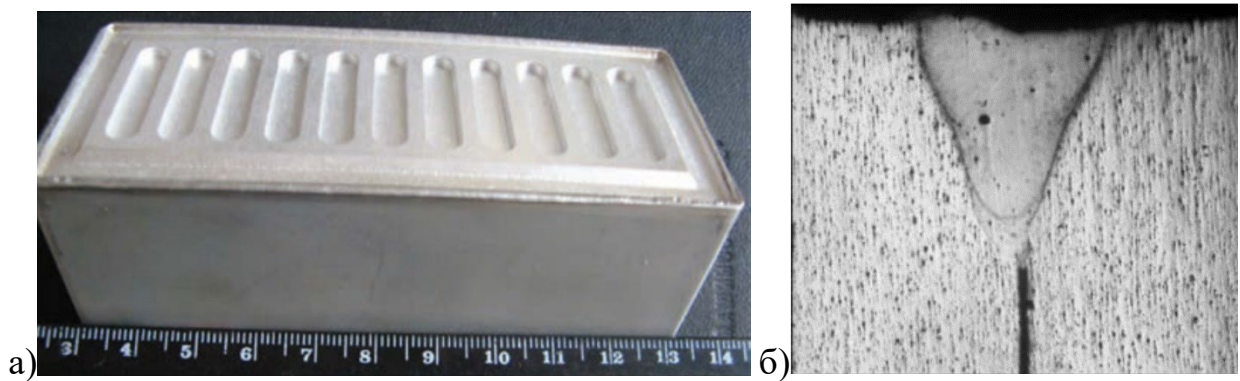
Приклади застосування лазерного та гібридного зварювання з ненаскрізним проплавленням: а) зовнішній вигляд фрагмента корпусу акумулятора з алюмінієвого сплаву АМг6 завтовшки 0,8 мм, з'єданого лазерним зварюванням [89]; б) макроструктура ( $\times 25$ ) перерізу торцевого з'єднання сплаву АМг6 ( $\delta=1,4$  мм), виконаного гібридним лазерно-плазмовим зварюванням зі швидкістю 168 м/год [88]
